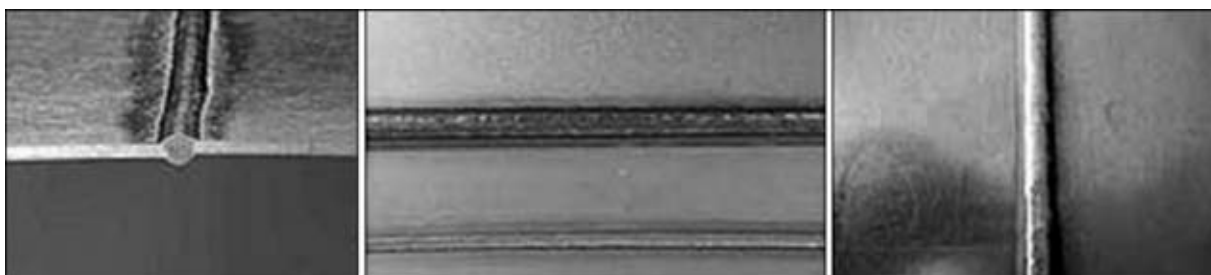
Внешний вид сварных швов при использовании СМТ процесса
